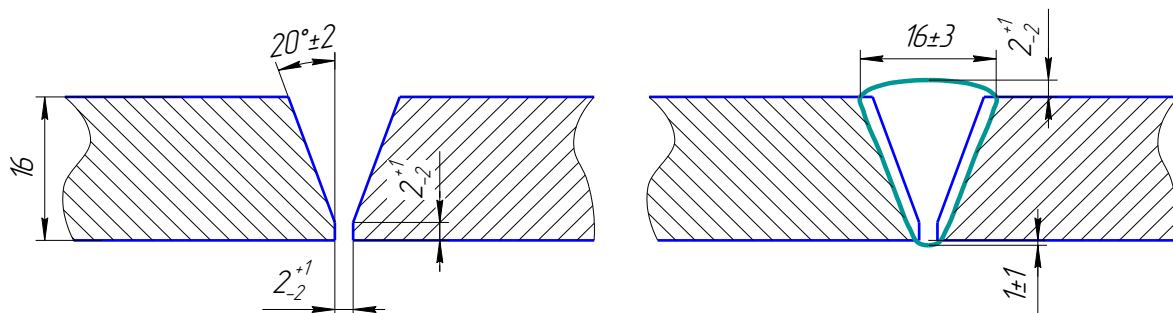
ГОСТ 14771-76, геометрические размеры сварного шва
